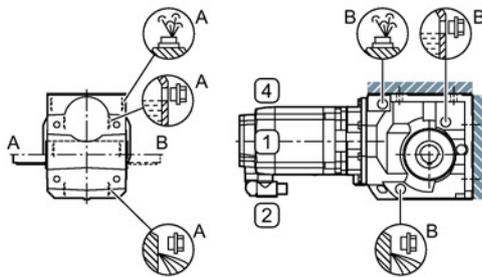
Einbaulagen für Stirradschneckengetriebe C, Fußausführung, Baugröße 29, 2-stufig
